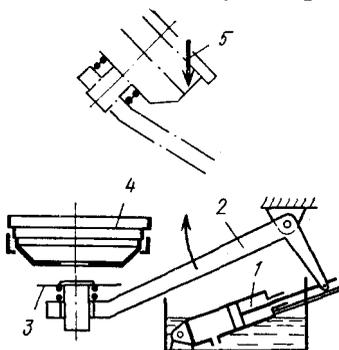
Схема подачи колеса в зону сварки
